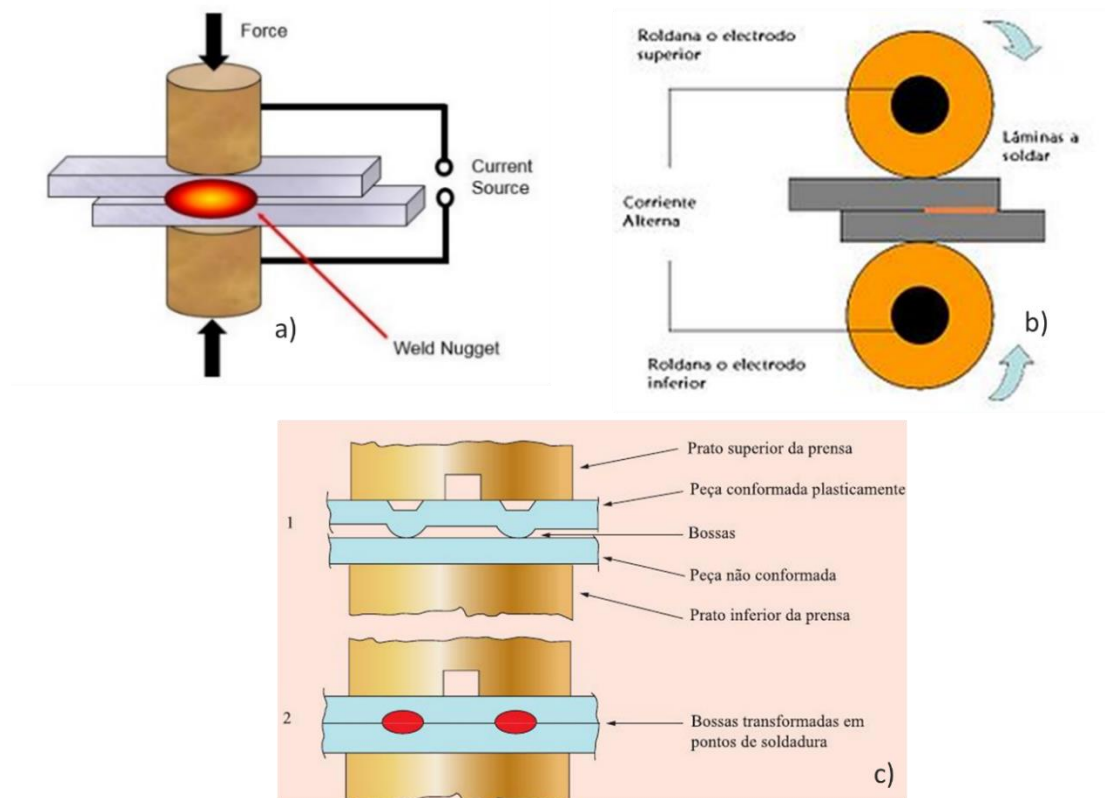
Soldadura por pontos a) soldadura por pontos b) soldadura contínua através de roletes c) soldadura por bossas [14, 23]
